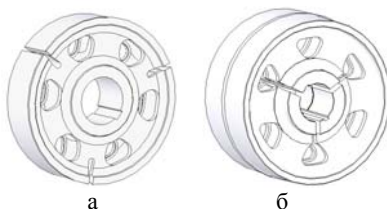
Схемы конструкций центров колес с компенсационными пазами на ободе (а) и на ступице (б)
